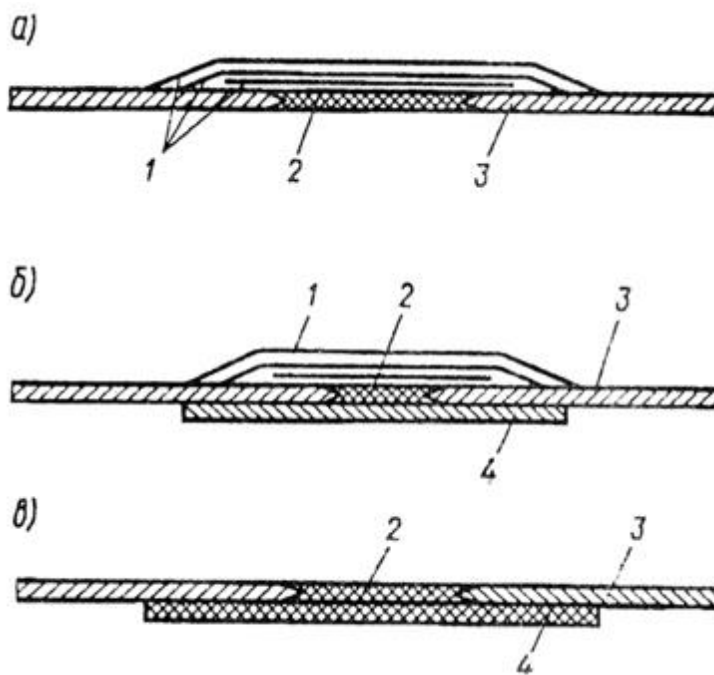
Варианты устранения сквозных повреждений в панелях кузова путем установки накладок из стеклоткани: а - установка накладок в 3 слоя; б - использование внутренней подкладки, предупреждающей вдавливание стеклоткани в отверстие; в - установка внутренней накладки из стеклоткани при устранении небольших отверстий; 1 - слои накладки из стеклоткани; 2 - слой эпоксидной смолы; 3 - металлическая поверхность кузова; 4 - металлическая подкладка с внутренней стороны
